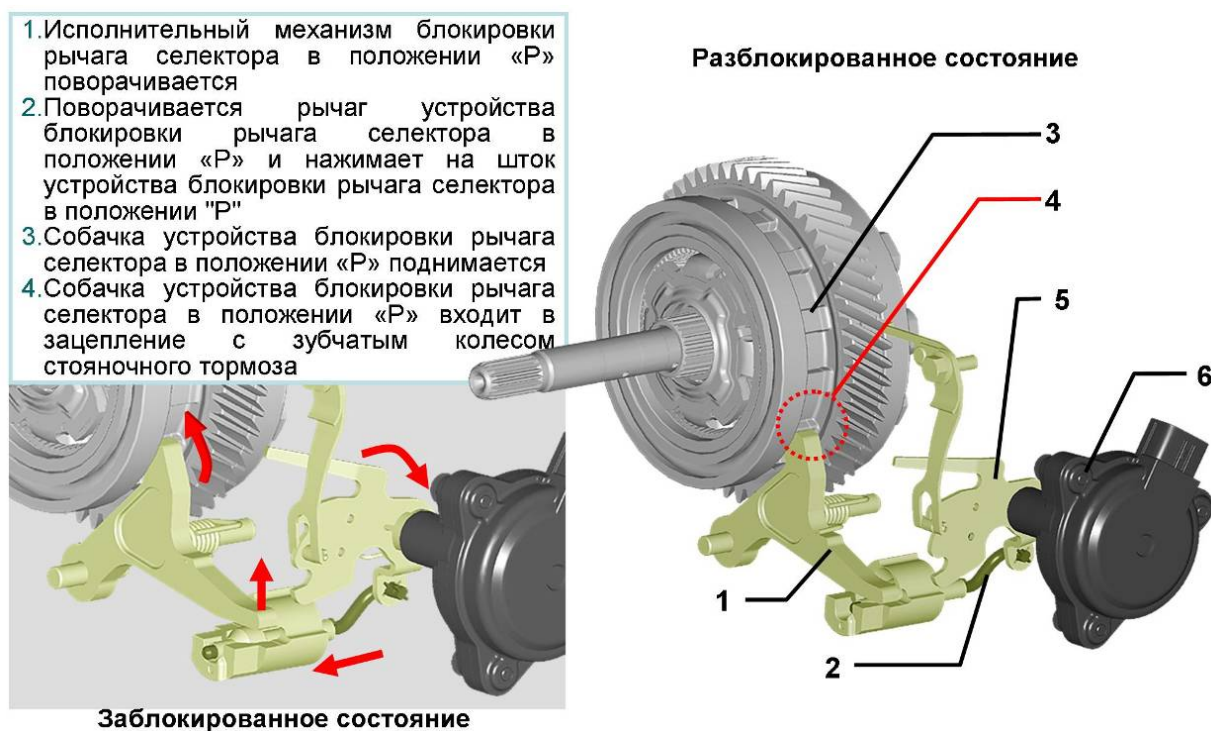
Механизм блокировки рычага селектора в положении «Р»: 1 - собачка; 2 - шток; 3 - зубчатое колесо стояночного тормоза; 4 - зацепление; 5 - рычаг
